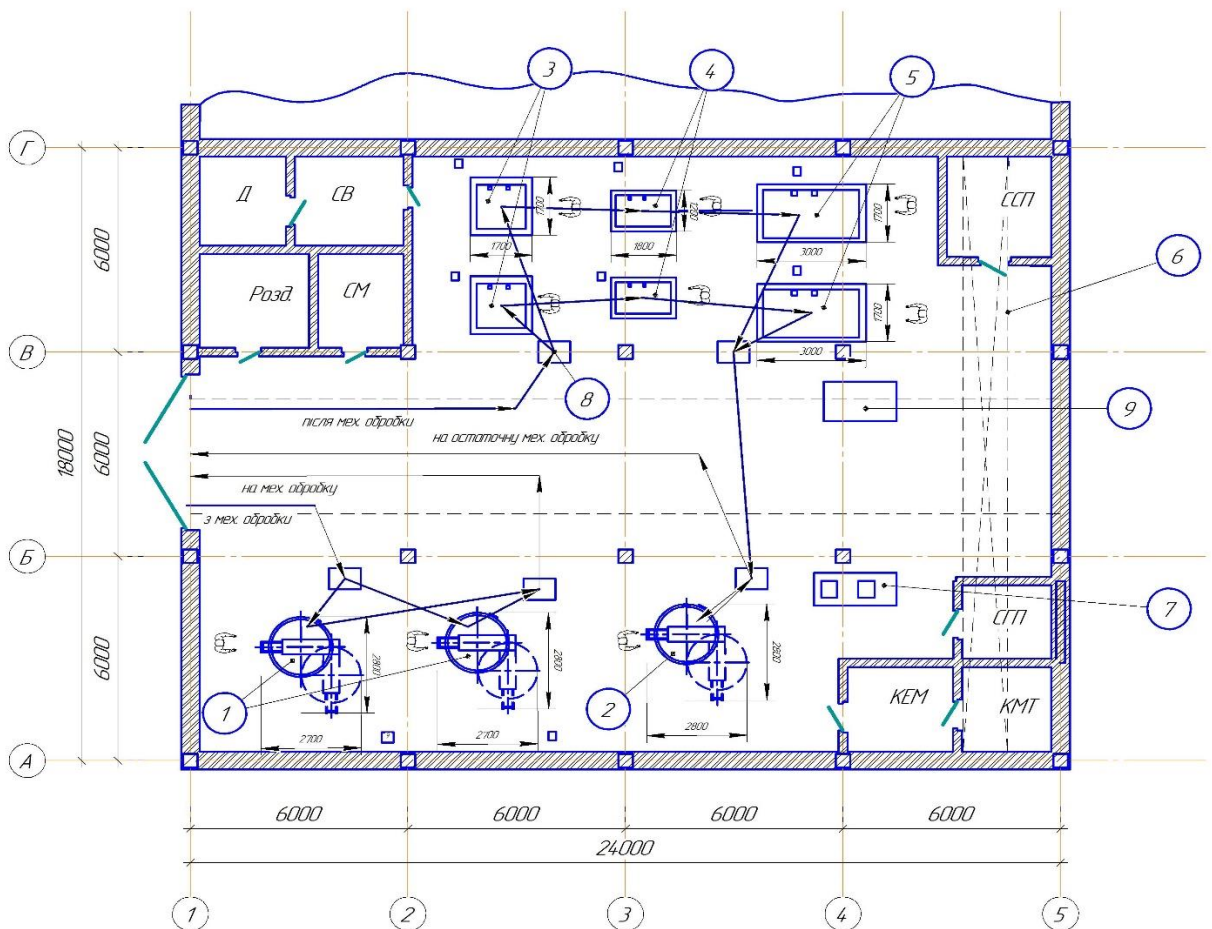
Планування ділянки цеху для термічної обробки черв'ячної фрези:
